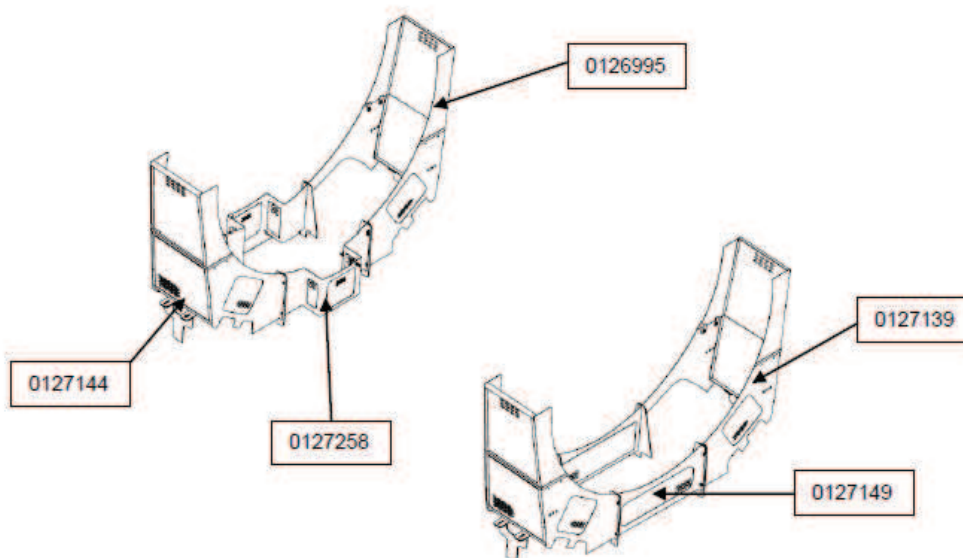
Montagem das proteções do banco de roletes / Montaje de las protecciones del banco de rodillos / Assembly of the guards at the roller bench / Montage des protecteurs sur le porte rouleaux
